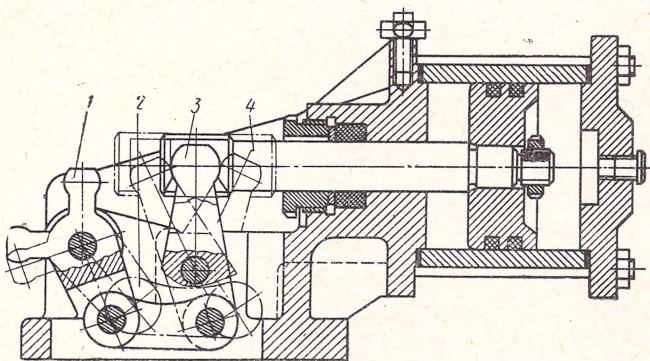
Гидравлический привод для безопасной работы на фрезерном станке
